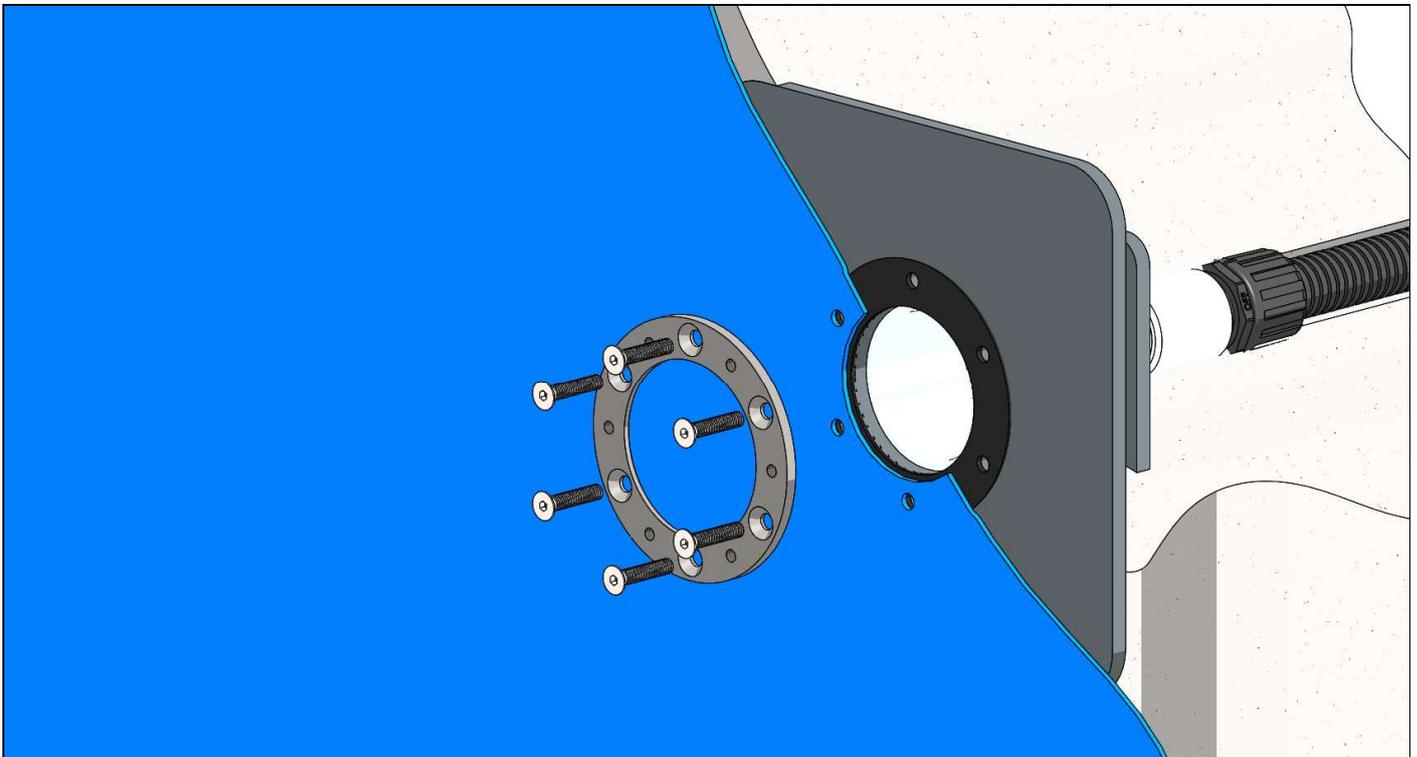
Montage de la bague de serrage – veiller à placer le joint plat sous le liner !
